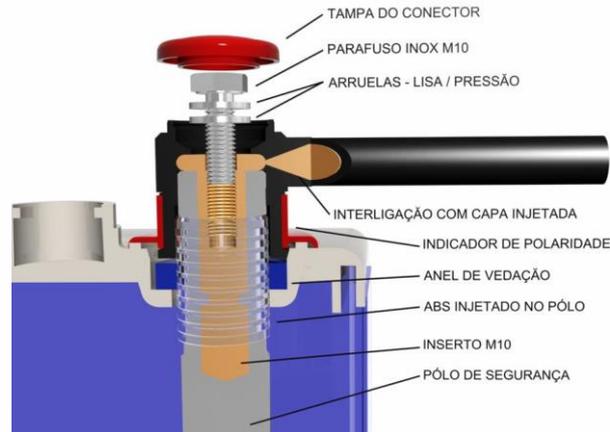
Vedação Polo Tampa – Desenho Ilustrativo “A”
